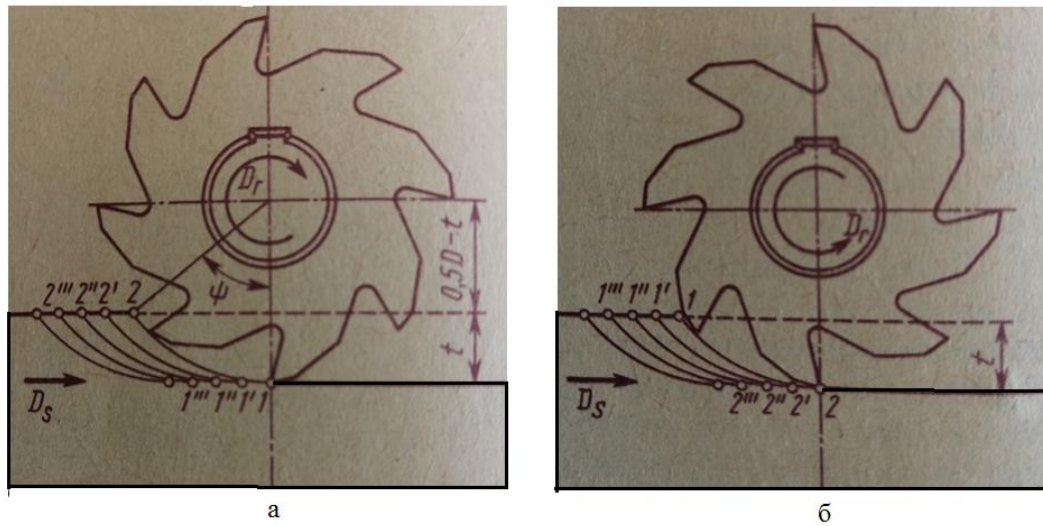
Зустрічний (а) і попутній (б) методи фрезерування
